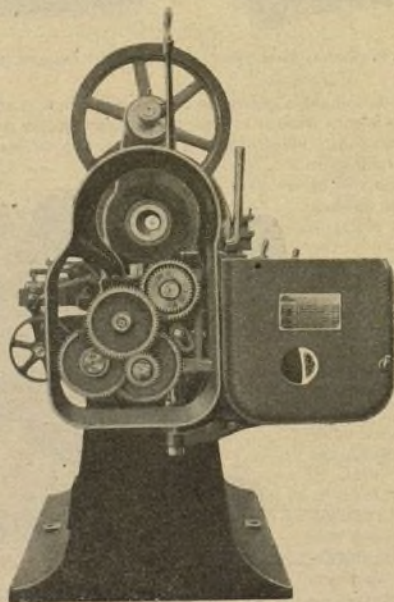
Engranajes de los avances del torno «Gisholt».
